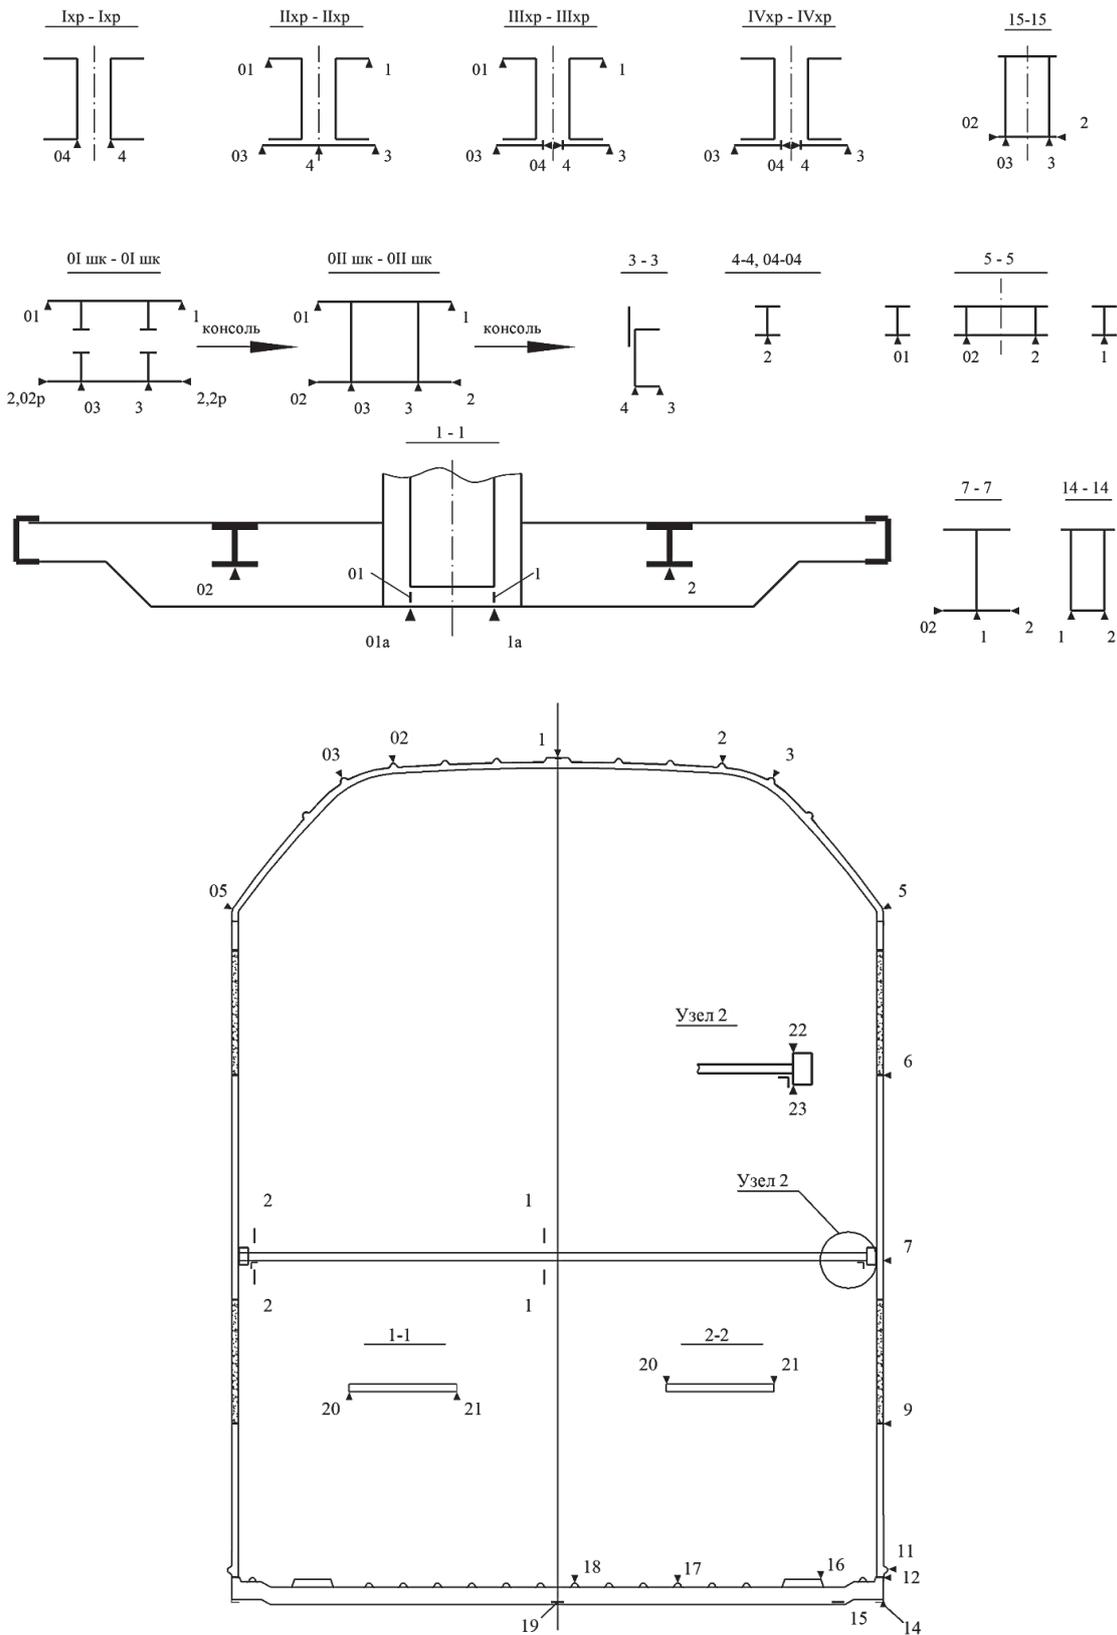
Схемы расположения тензодатчиков на основных несущих элементах металлоконструкции кузова вагона
